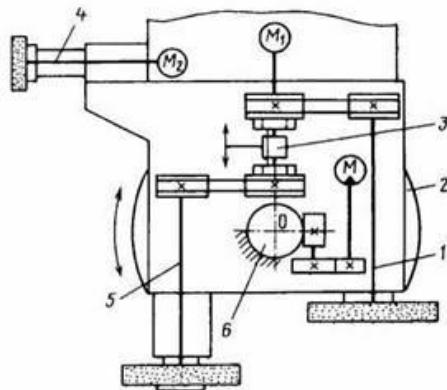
Кинематическая схема револьверной головки карусельно-шлифовального станка
